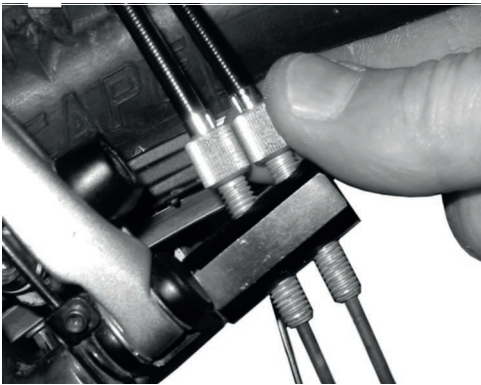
ROHLOFF-Naben Versionen mit interner Schaltansteuerung haben die Zugeinsteller am Zuggegenhalter
